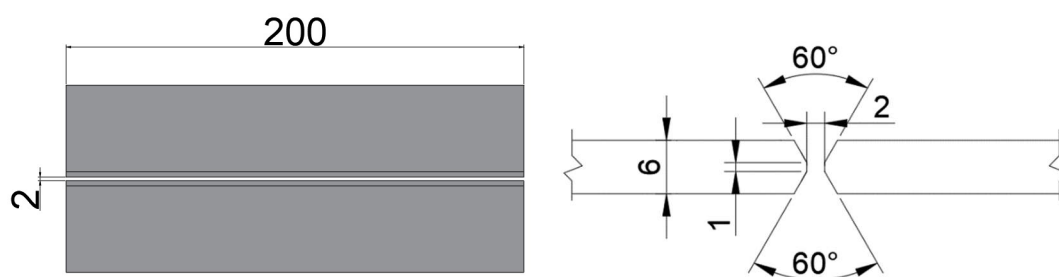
Ilustração esquemática da junta de soldadura da amostra F.
